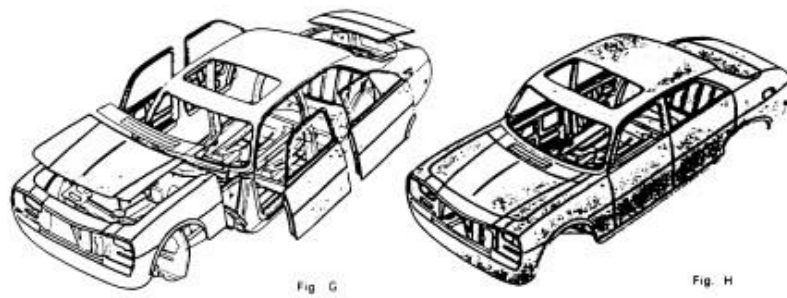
Ensamblado de los elementos desmontables sobre la carrocería.
